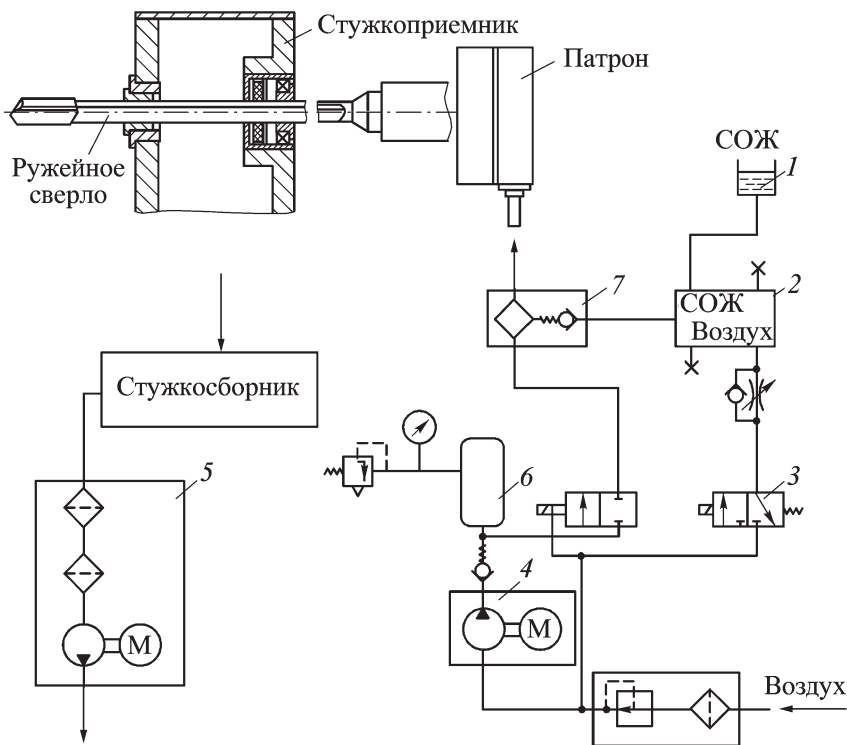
Схема установки для подвода аэрозоли в зону резания ружейного сверла:
